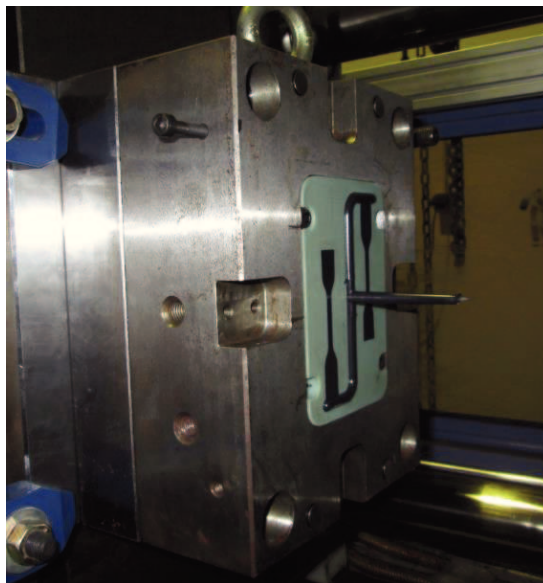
Peças de PP T20 injetadas em molde ABS Digital (superfície moldante)
